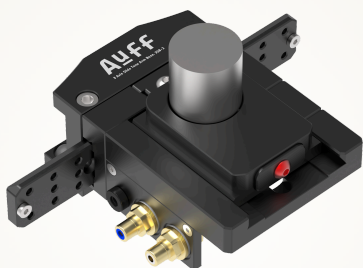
① Emplacement du boulon de blocage arrière — serrez ici pour fixer
